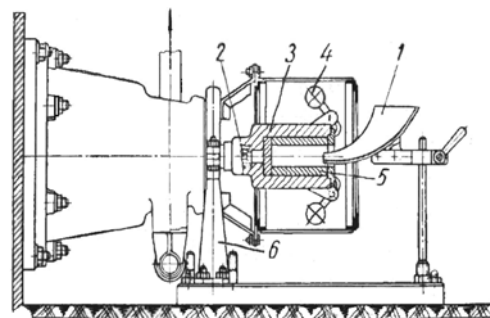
Схема установки для отримання вкладиша підшипника ковзання: 1 – заливочна воронка; 2 – шток виштохувача; 3 – виливниця; 4 – відцентровий затвор; 5 – виливок; 6 – упорний люнет
